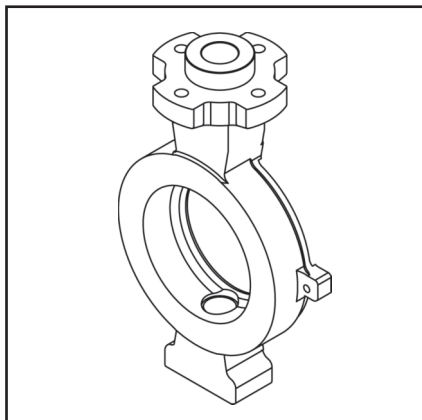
Vista Explodida do Subconjunto do Corpo
